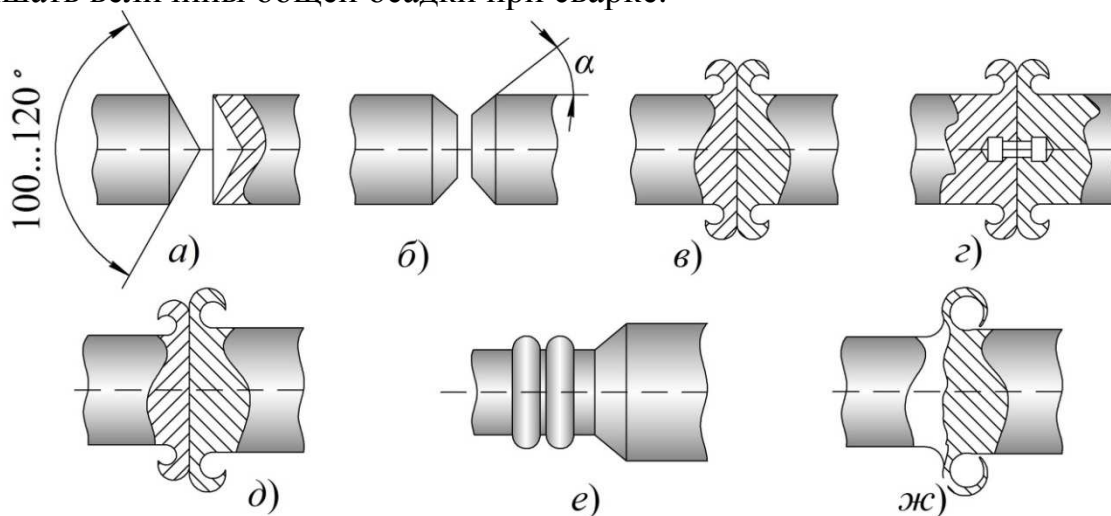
Варианты подготовки торцов заготовок сплошного сечения для сварки трением
